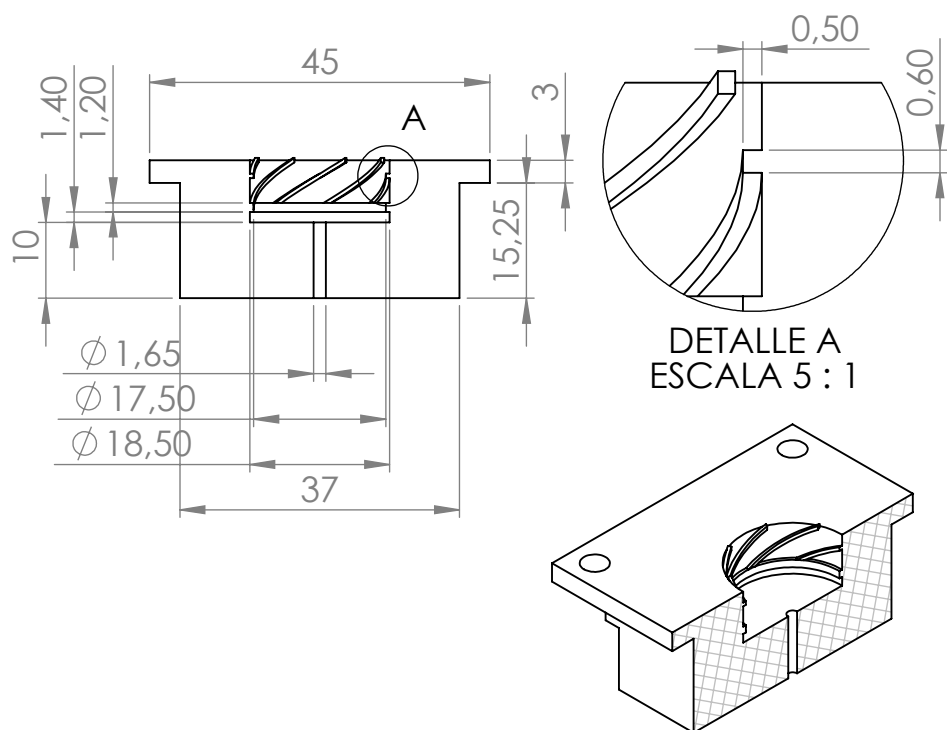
Vista en corte del molde del *Robot Rotator* parte A
